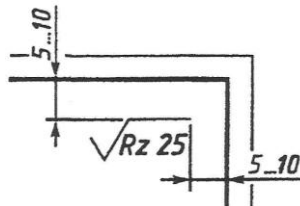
Обозначение шероховатости, одинаковой для всех поверхностей изделия
